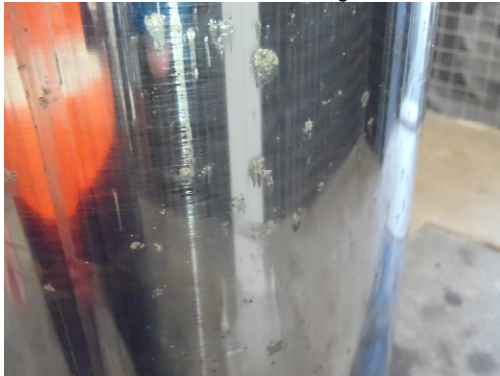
lichte krassen in cilinderstang – detail 1
